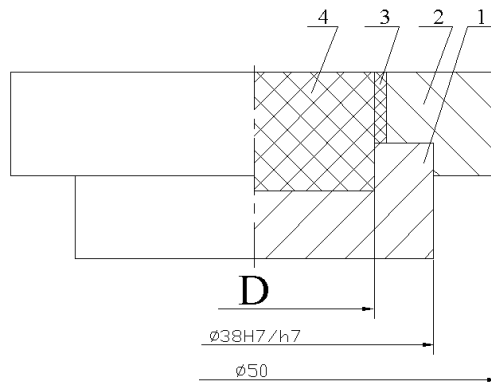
Форма для виготовлення зразків: 1 - корпус; 2 - кришка; 3 - пластмасове кільце; 4 - метало-полімер
